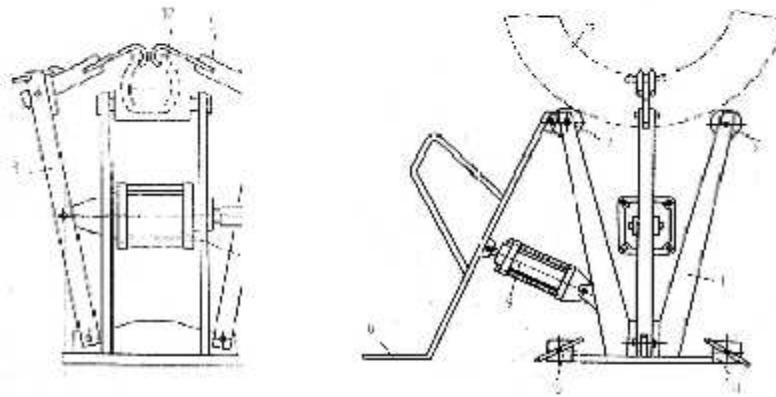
Устройство для осмотра и ремонта покрышек
